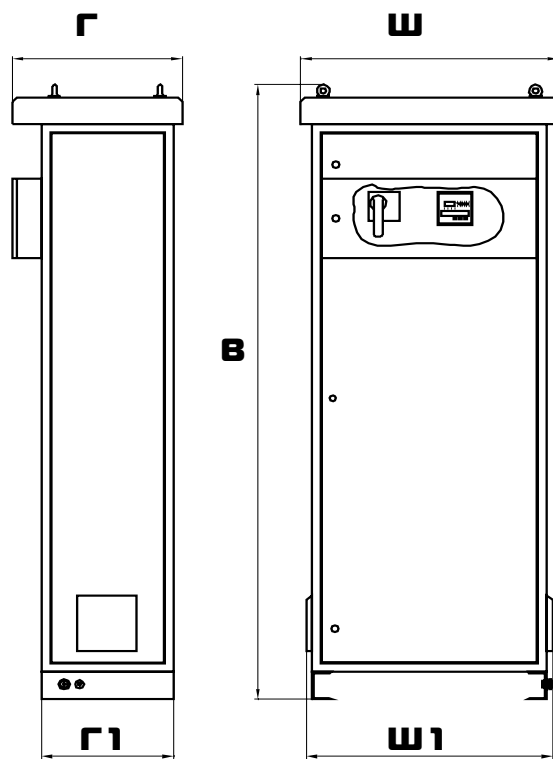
Габаритный чертеж КРМ-0,4 (500-800 кВАр) IP20, IP40
